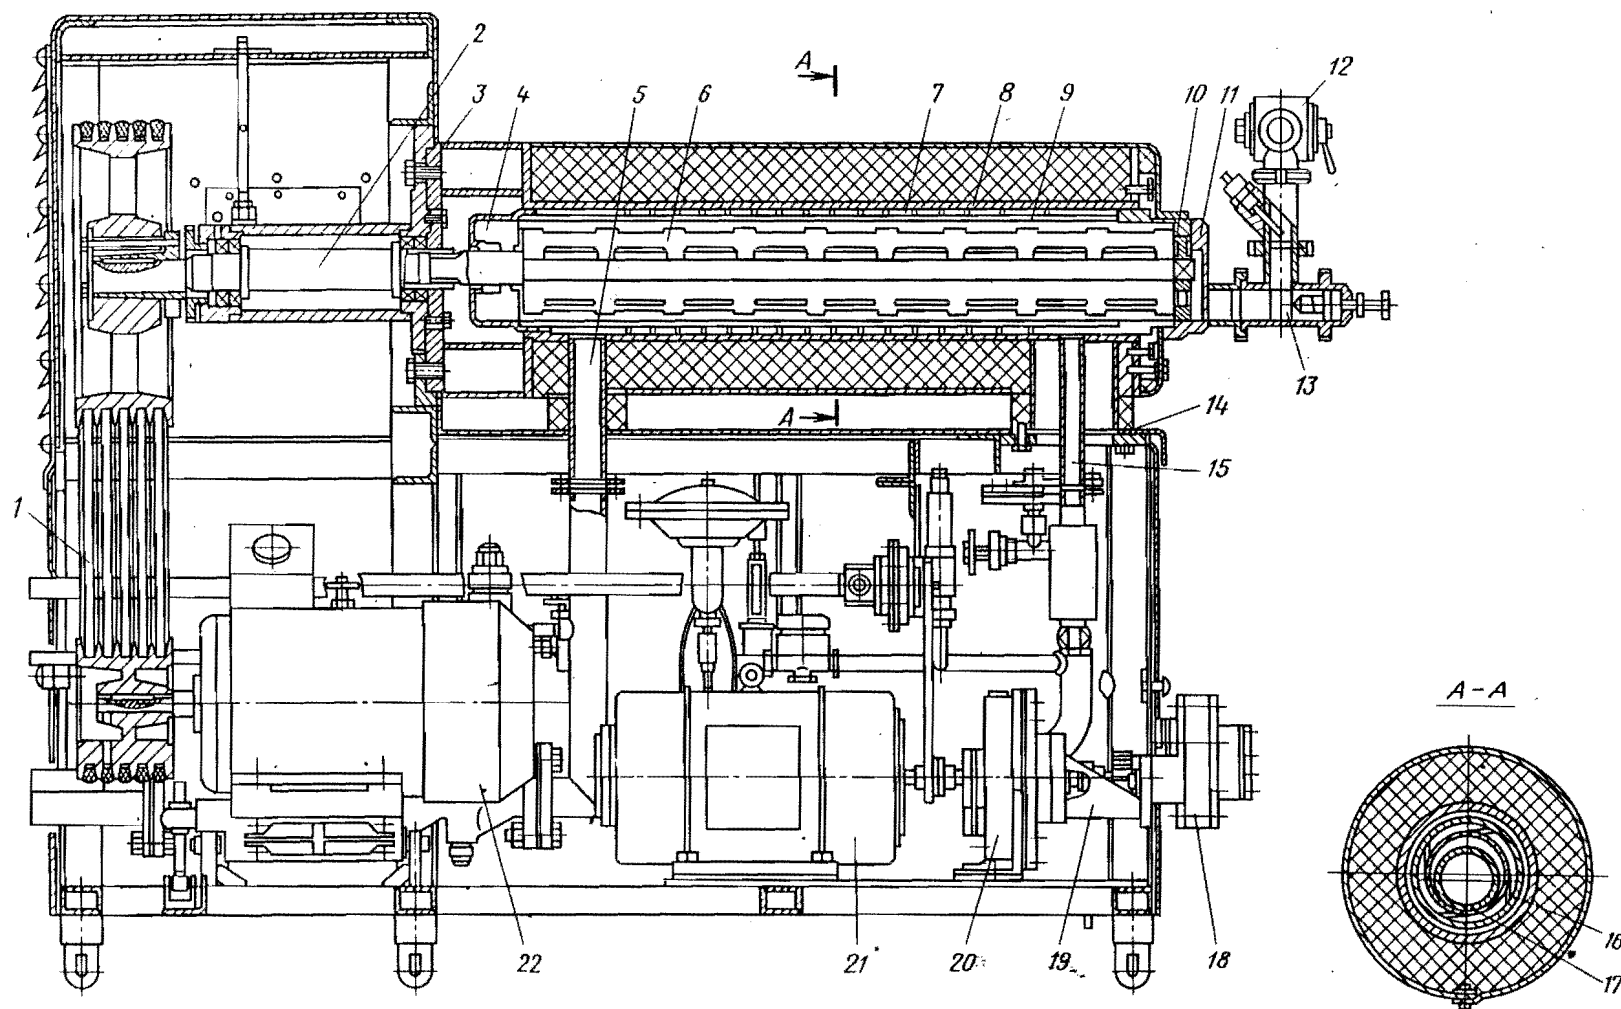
Общий вид цилиндра фризера марки Б6-ОФШ:
